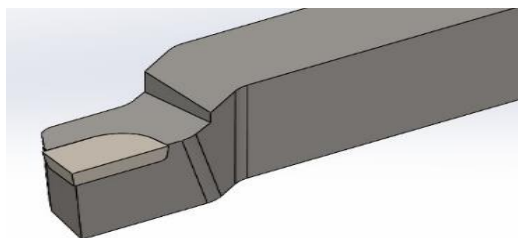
Токарный подрезной резец с пластиной из твердого сплава ВК8
